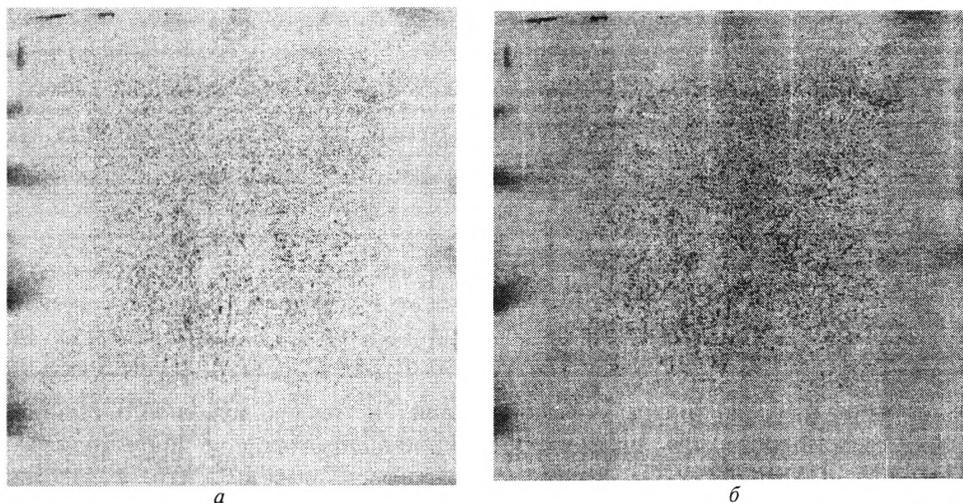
Макроструктура литой заготовки стали 70К, полученной при производстве кордовой стали без вакуумирования: а – при разливке с закрытой струей; б – при разливке с открытой струей
